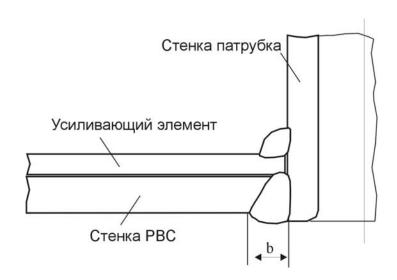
Схема сварного шва сопряжения люка- лаза со стенкой РВС
